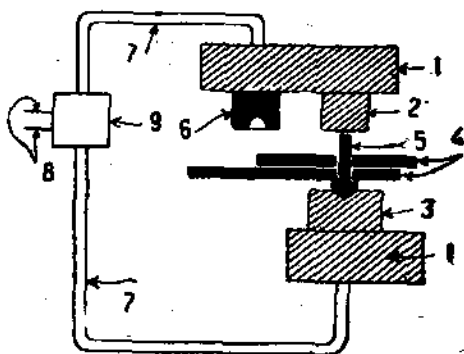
Клепка при помощи аппарата для точечной сварки.
